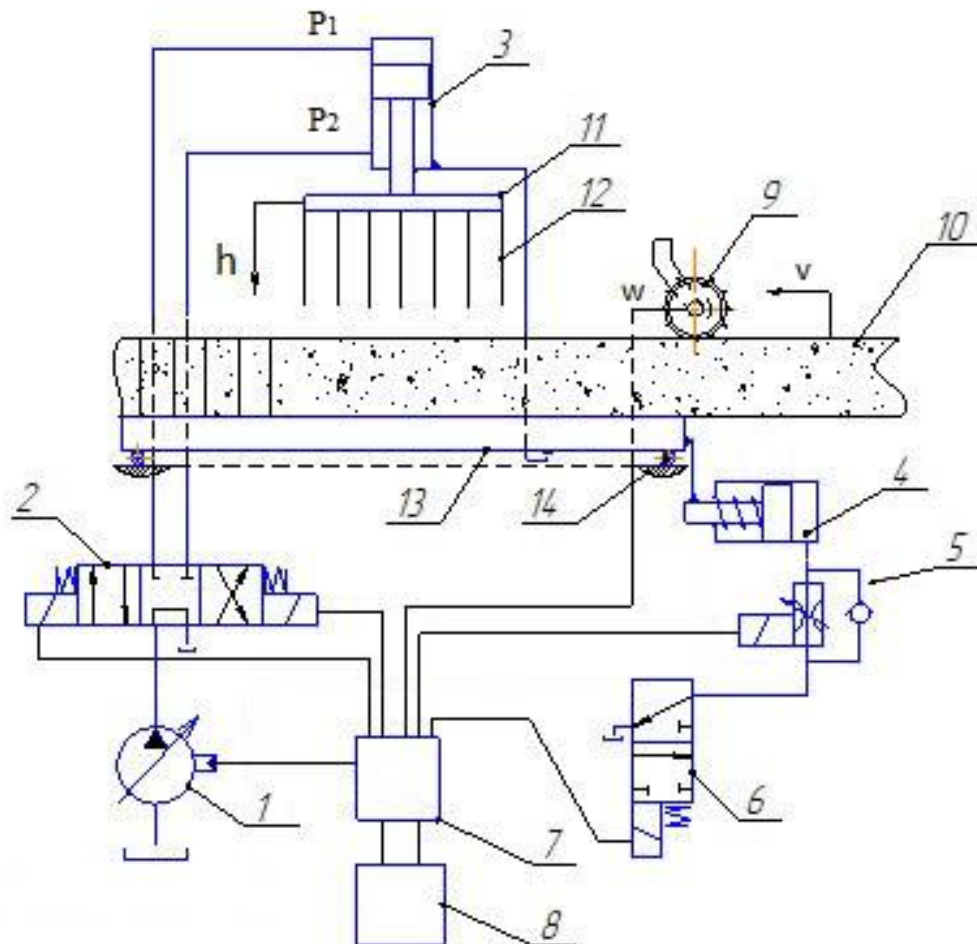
Гідравлічна схема автоматизованого пристрою для формування заготовки цегли
